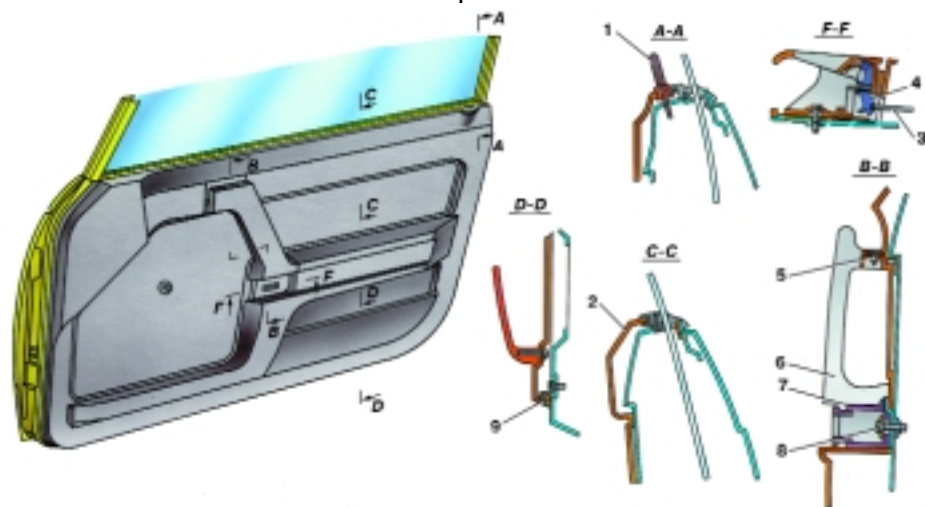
Установка обивки боковой двери: 1 – кнопка блокировки замков; 2 – обивка; 3 – тяга внутреннего привода; 4 – поводок ручки внутреннего привода; 5 – винт верхнего крепления поручня; 6 – поручень; 7 – ручка внутреннего привода; 8 – винт нижнего крепления поручня; 9 – винт крепления обивки
